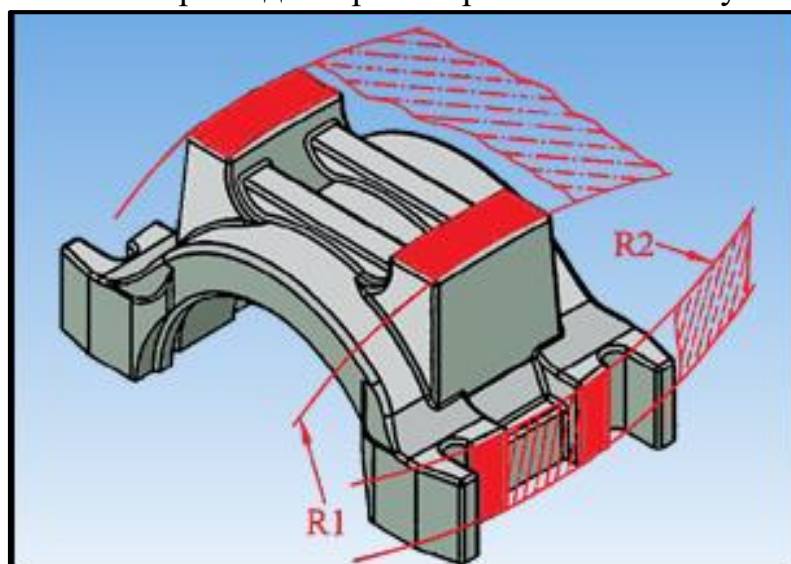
Общий вид адаптера с опорными R1 и упорными R2 поверхностями.
